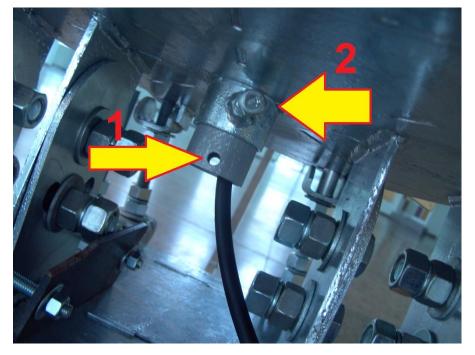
Fixação do Suporte do Alimentador no Regulador.
